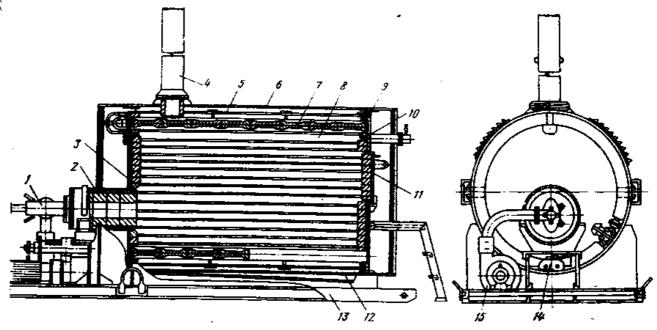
Трубчатый битумонагреватель: 1 – форсунка; 2 – топка; 3, 10 – передняя и задняя торцовые стенки; 4 – дымовая труба; 5, 6, 12 – кожухи; 7 – вставка; 8 – трубы; 9 – кольцо; 11 – окно; 13 – рама; 14 – соединительный кран; 15 – дутьевой вентилятор
